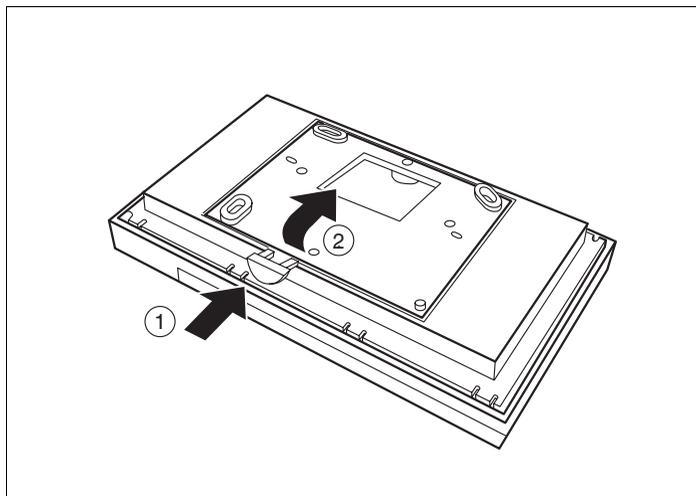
Staccare l'unità di servizio dalla piastra di montaggio
